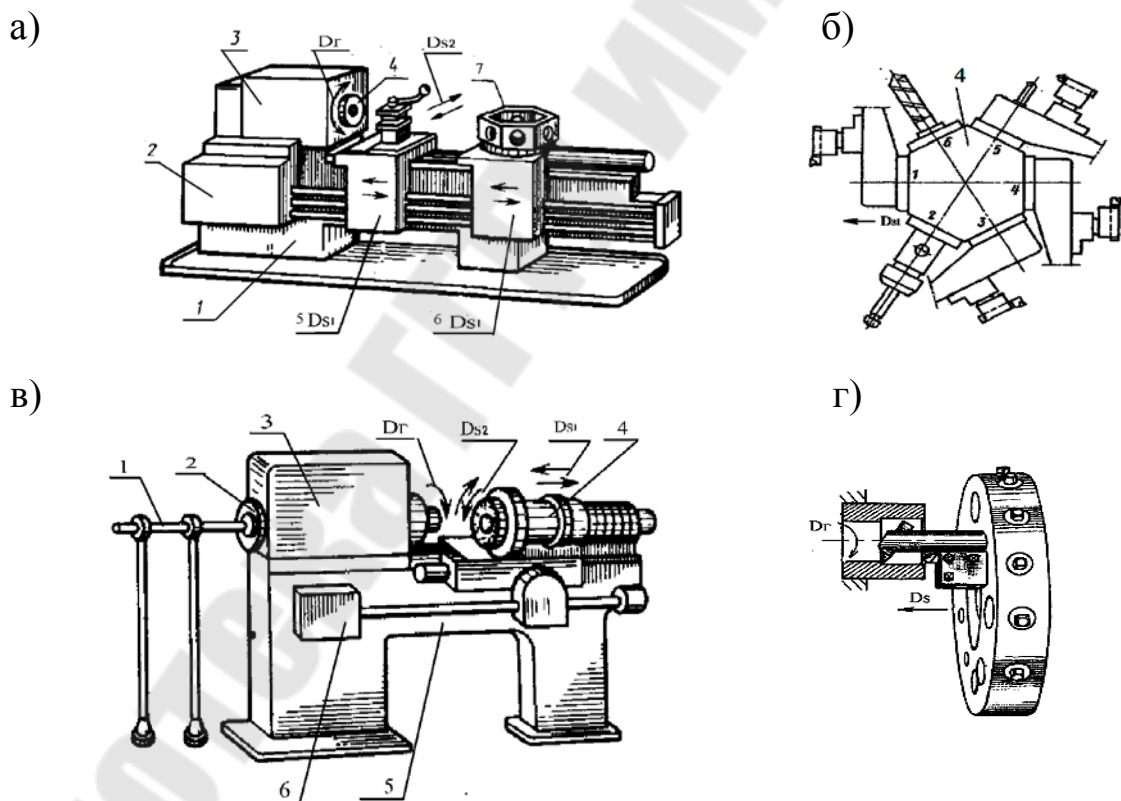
Компонировка токарно-револьверных станков (а, в) и закрепление инструмента в револьверной головке (б, г)
